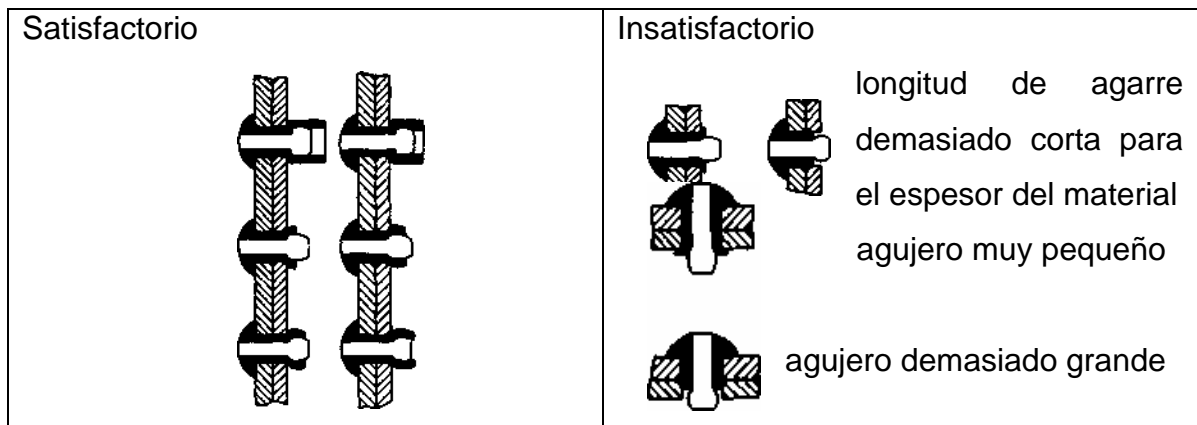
Inspección de los remaches de acción automática (cierre de fricción)
